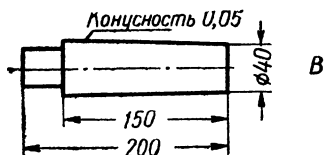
Схема установки детали для обтачивания конической поверхности способом сдвига задней бабки.
